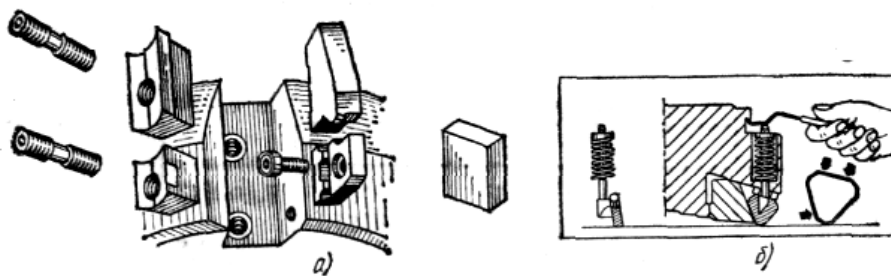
Схема базування багатогранних пластин на торцевих фрезах та розточувальному інструменті
